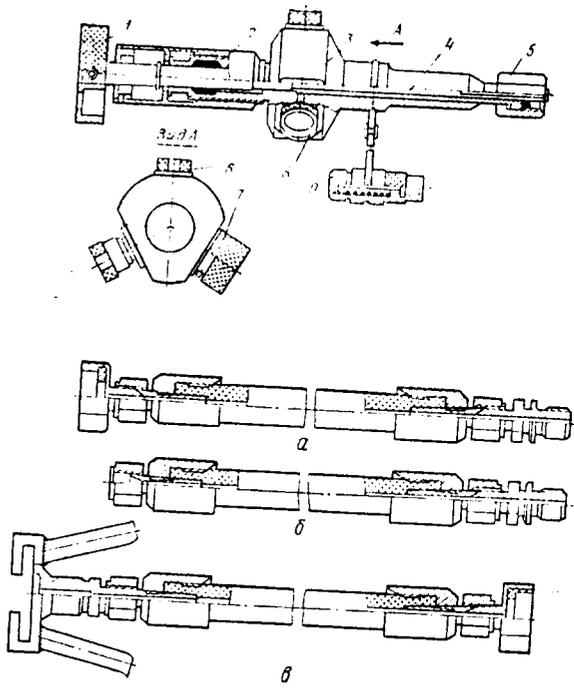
Приспособление № 63740/028 для проверки давления в стойках и шинах:
